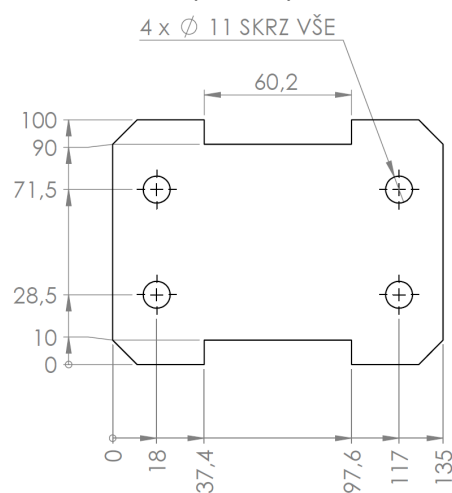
Provedení držáku na tažné zařízení, převzato z [3]
